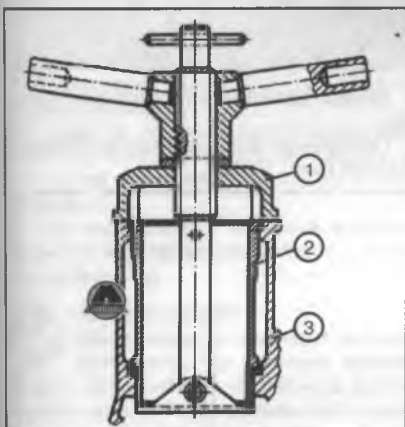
Съемник для выпрессовки гильзы из блока цилиндров: 1. Съемник; 2. Гильза; 3. Блок цилиндров.
